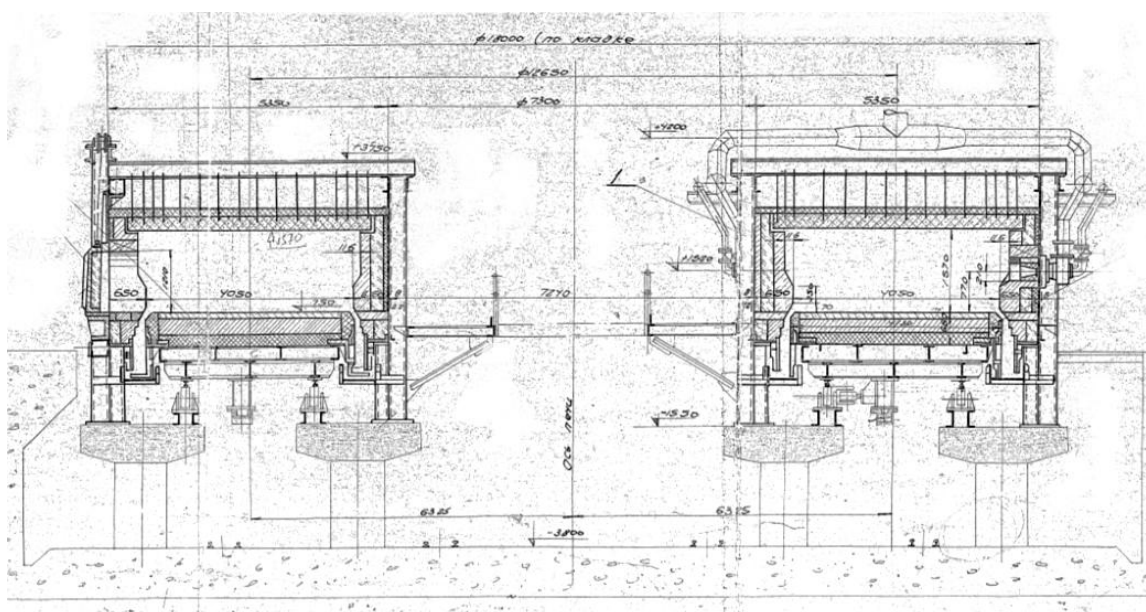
Кольцевая печь для нагрева заготовки перед раскроем ТПЦ-2 ОАО «ЧТПЗ»
